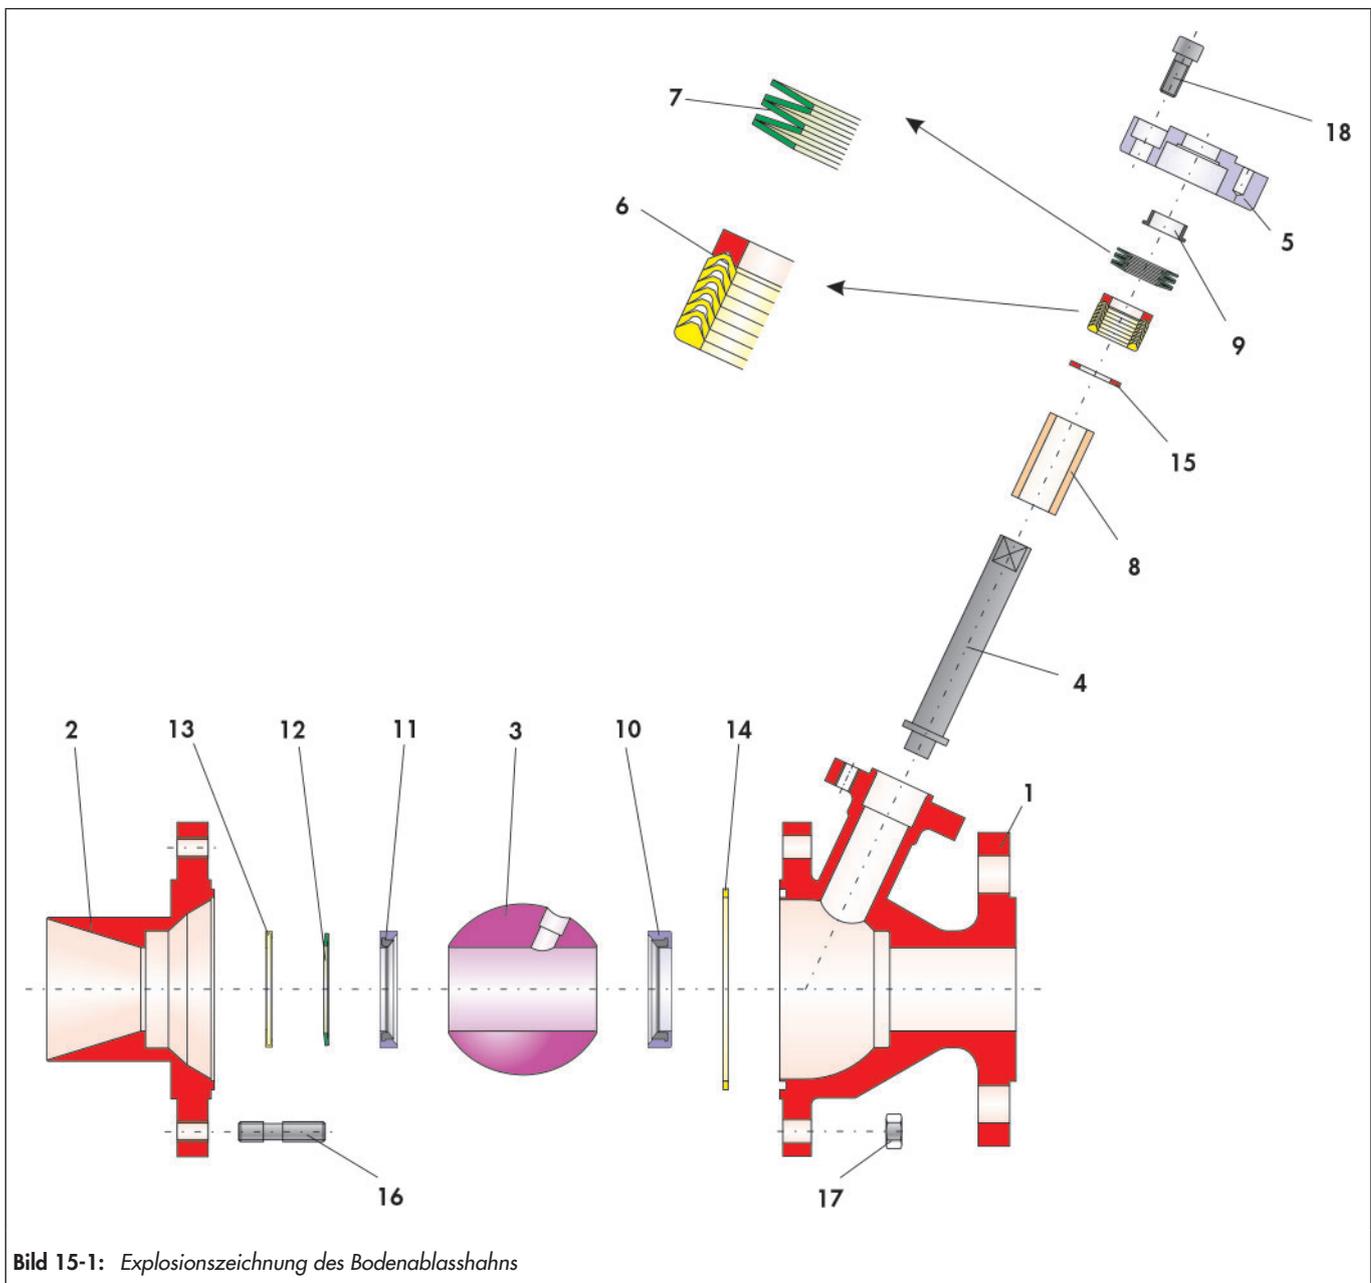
Explosionszeichnung des Bodenablasshahns
